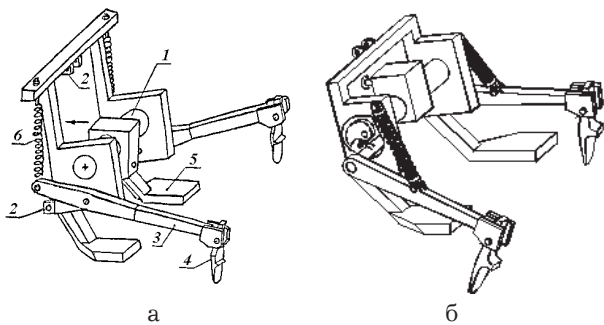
Общий вид динамического лункообразователя: а – лункообразователь типа Л-2У; б – лункообразователь типа Л-2М; 1 – остов, 2 – навесное устройство, 3 – качающийся рычаг, 4 – игла, 5 – лыжеобразный полз, 6 – пружина
